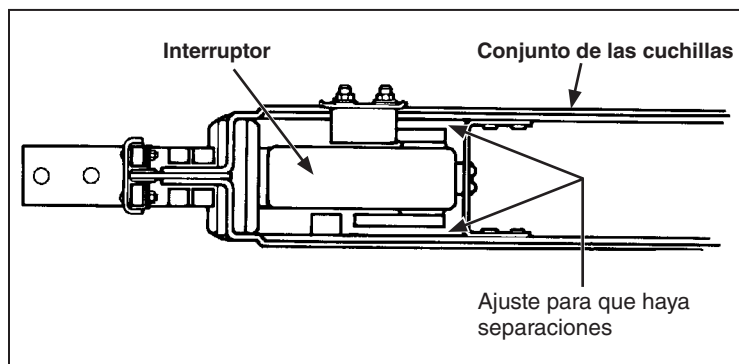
Conjunto de la cuchilla en posición de cierre total.
